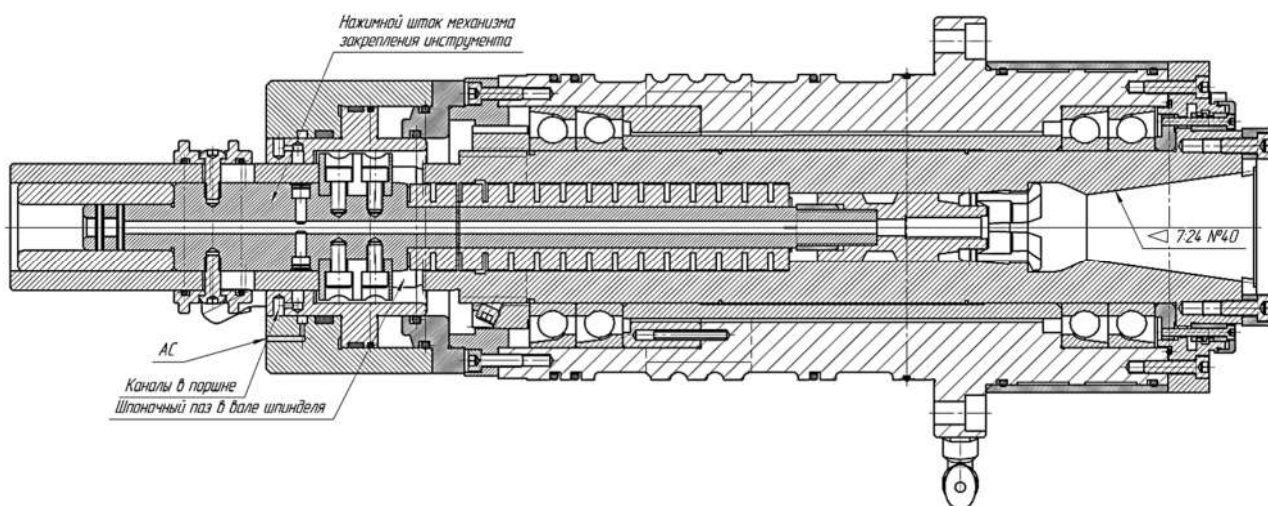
Пример типовой конструкции шпиндельного модуля для фрезерных станков с ЧПУ
